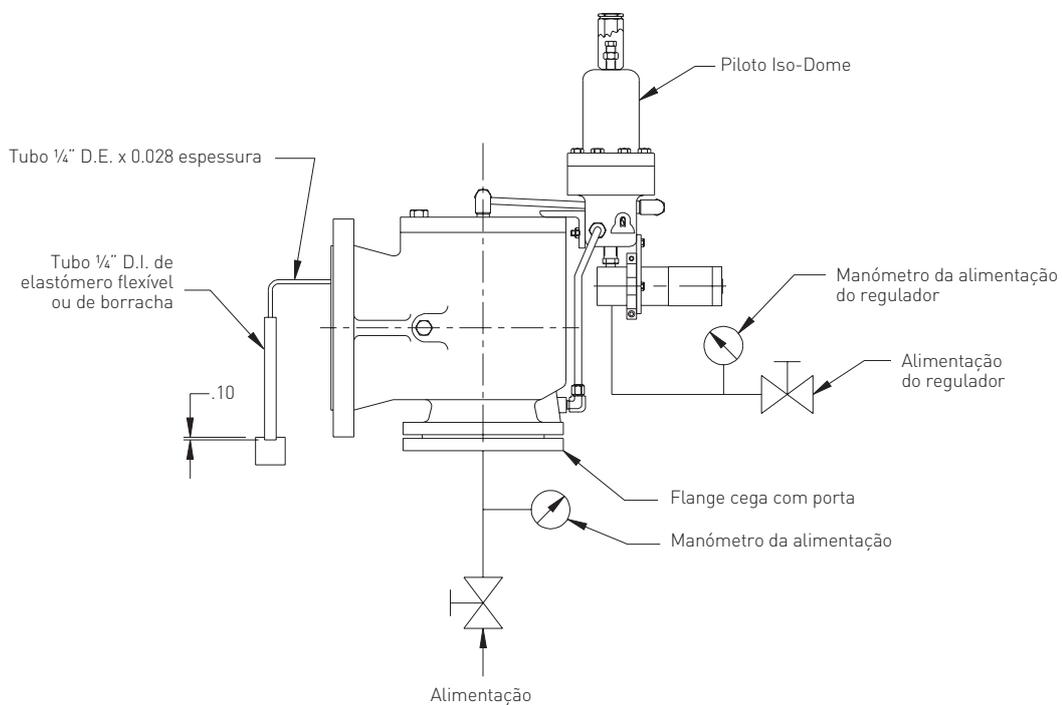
DISPOSITIVO DE ENSAIO PARA VÁLVULAS COM PILOTO ISO-DOME
